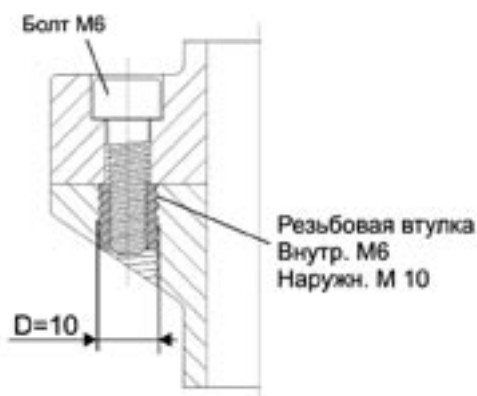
Ремонт резьбового отверстия с помощью резьбовой втулки
